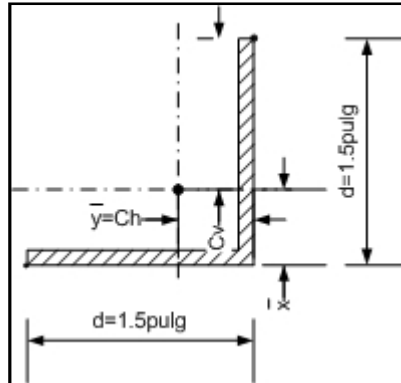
Diagrama del cordón de la soldadura a chaflán.
